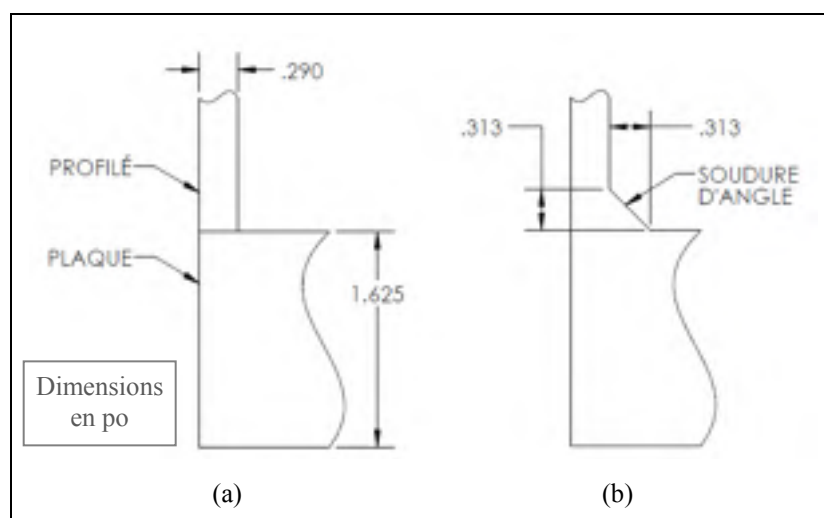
Géométrie typique en vue de coupe des joints avant (a) et après (b) le soudage
